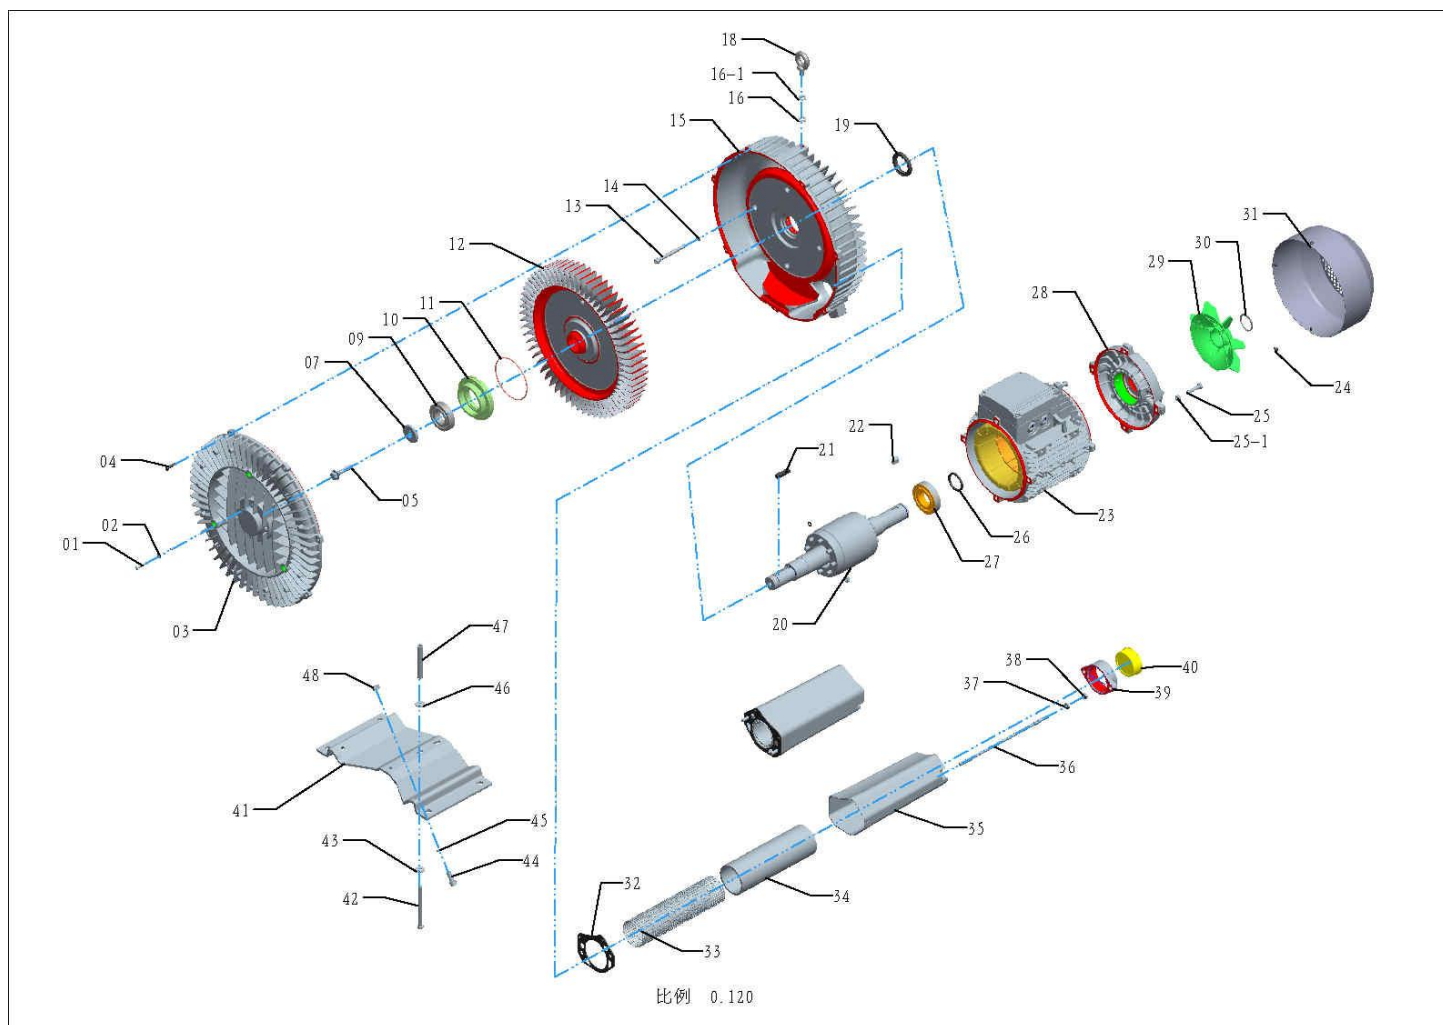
Деталировка одноступенчатых воздуходувок 2RB
